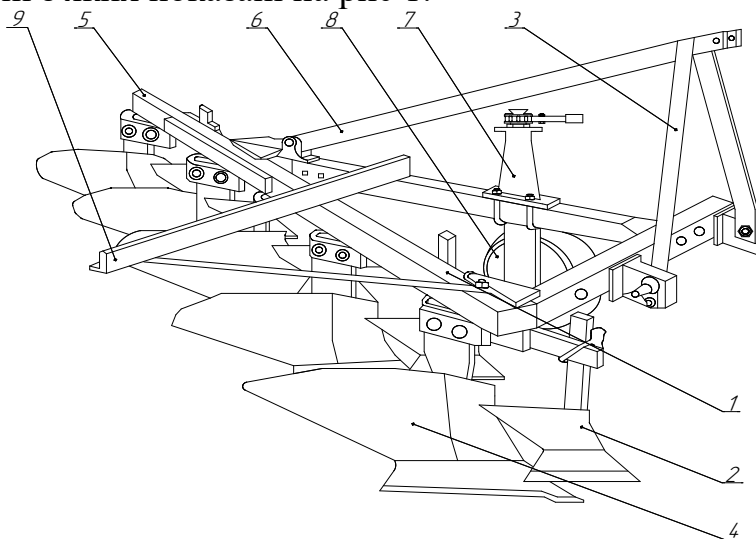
Плуг лемішний начіпний п'ятикорпусний ПЛН-5-35:
